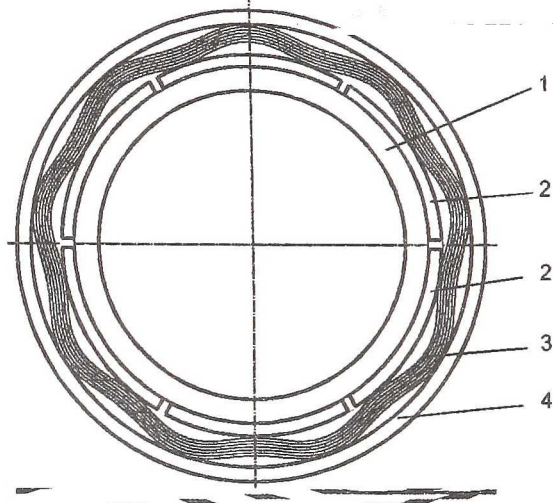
Управляемая упруго демпферная опора с пластинчатым демпфером; 1 - неразрезное кольцо; 2 - конусные сегменты; 3 - демпфер; 4 - корпус
